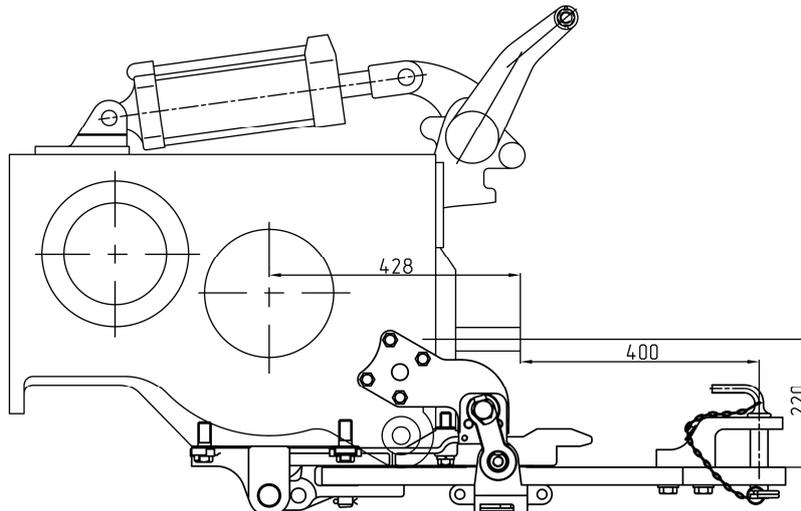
Schéma d'installation du dispositif TSU-1M (pendule)
